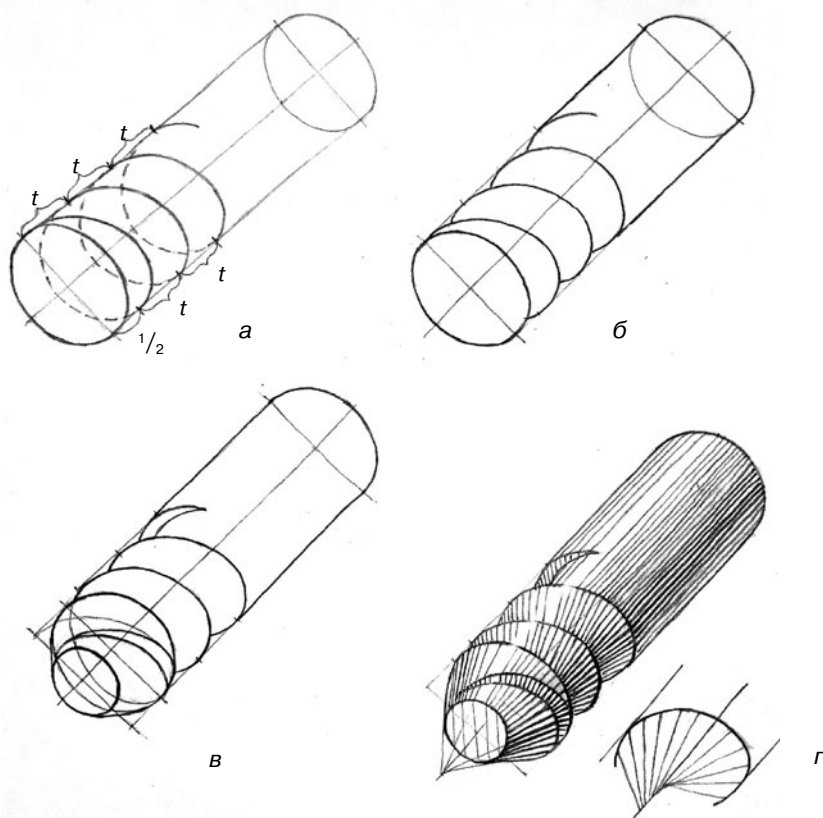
Этапы рисования цилиндрической винтовой линии и винтовой поверхности на стержне
